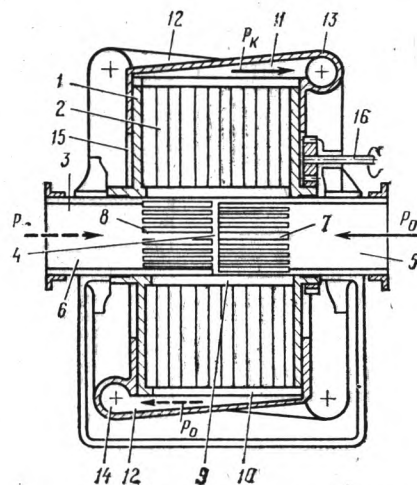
Конструкция обменника давления с радиальным размещением ячеек: 1 — ротор; 2 — ячейки; 3 — трубопровод; 4 — перегородка; 5, 6 — полости вала; 7, 8 — окна; 9, 10 — каналы во вставках; 11, 12 — коллекторы; 13, 14 — воздушный и газовый ресиверы; 15 — кожух; 16 — привод от дизеля
